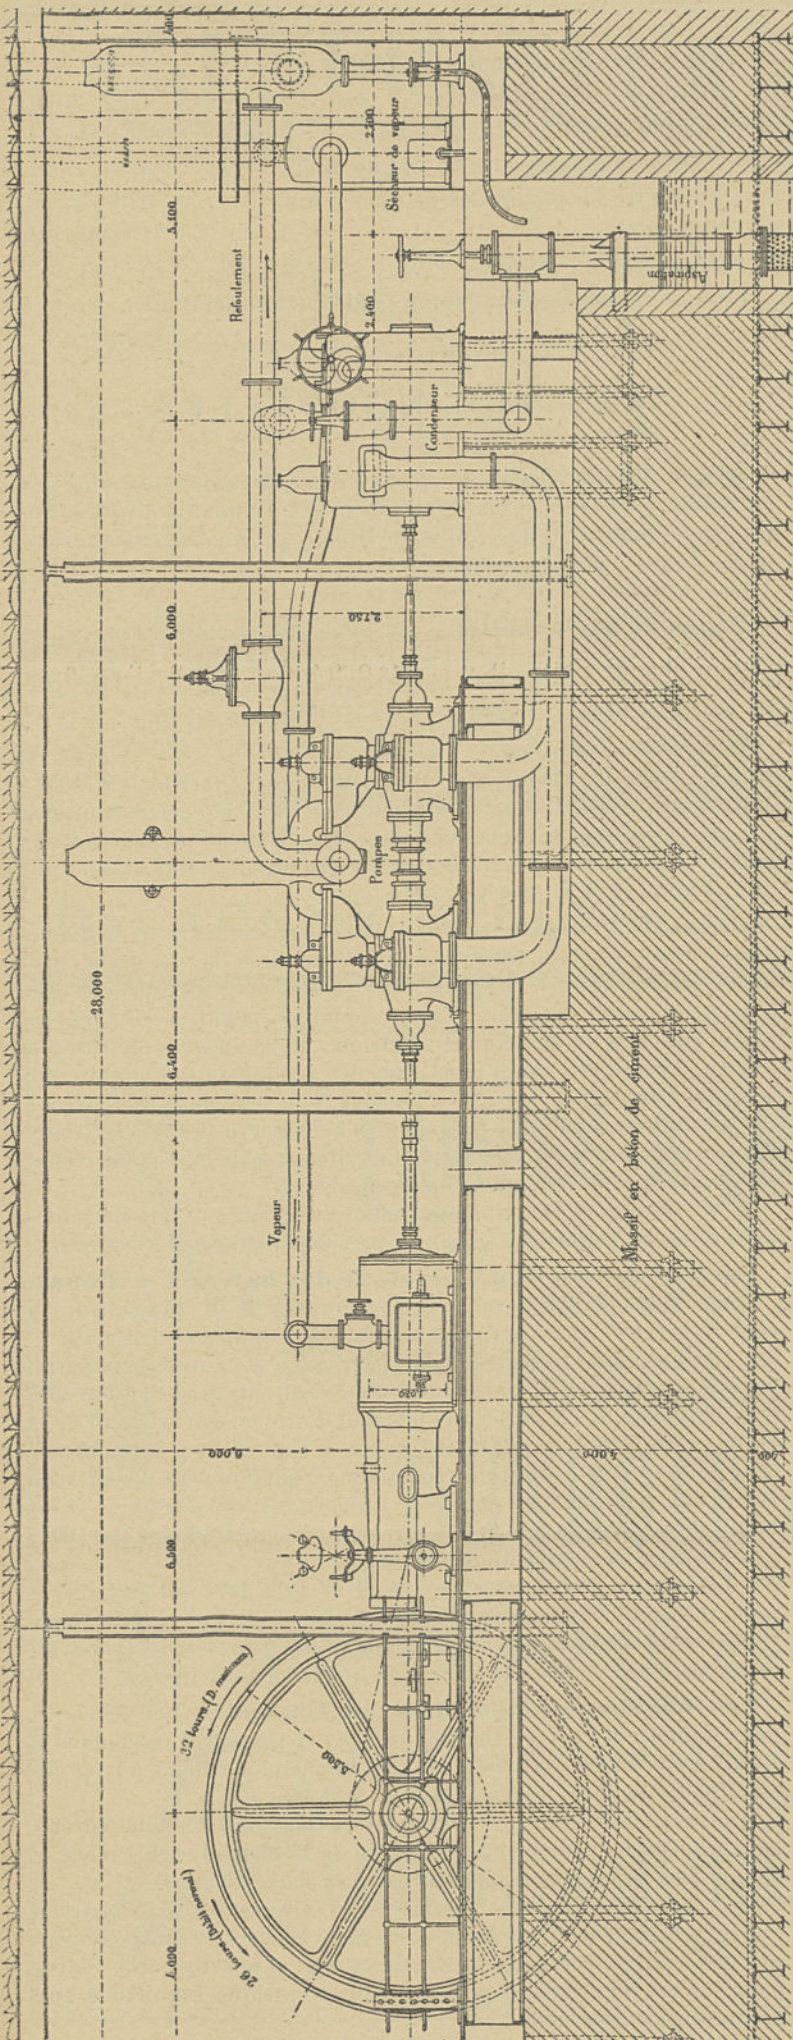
Pompe d'épuisement souterraine, de MM. Mailliet et C^e, d'Anzin. Elevation.
